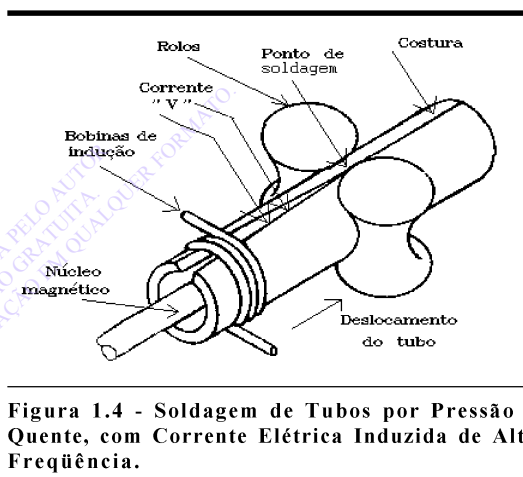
Soldagem de Tubos por Pressão à Quente, com Corrente Elétrica Induzida de Alta Frequência.
